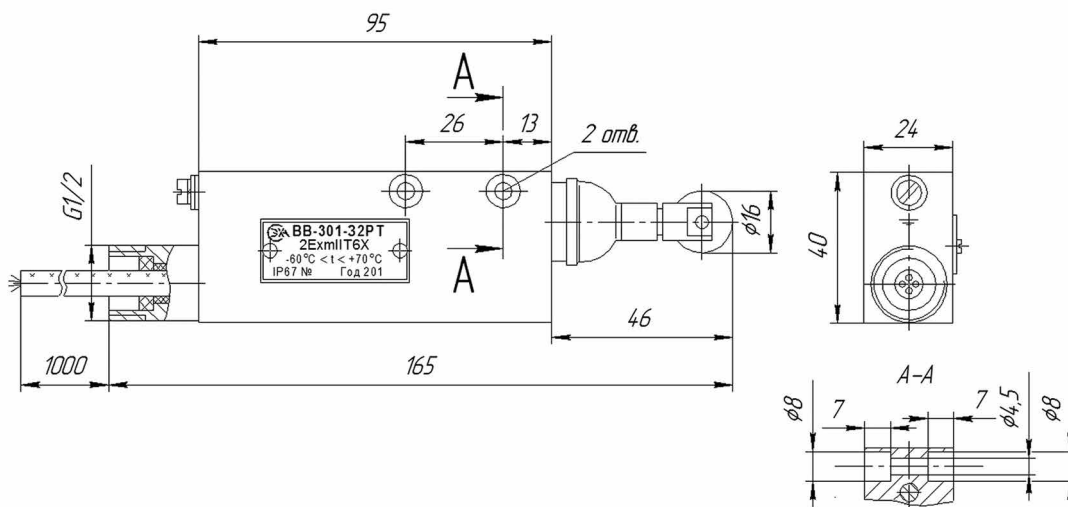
Габаритные и установочные размеры ВВ-301-32РТ
